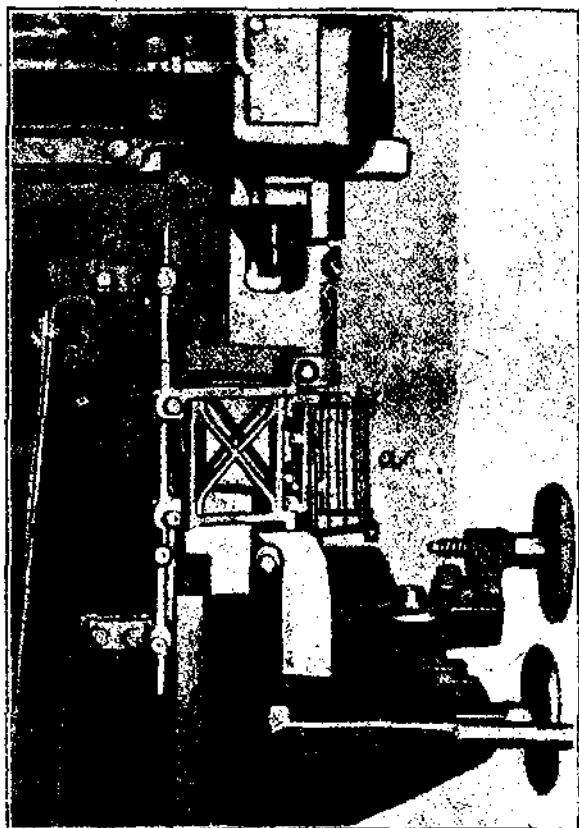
Направляющий прибор для работы на сверлильном станке.
